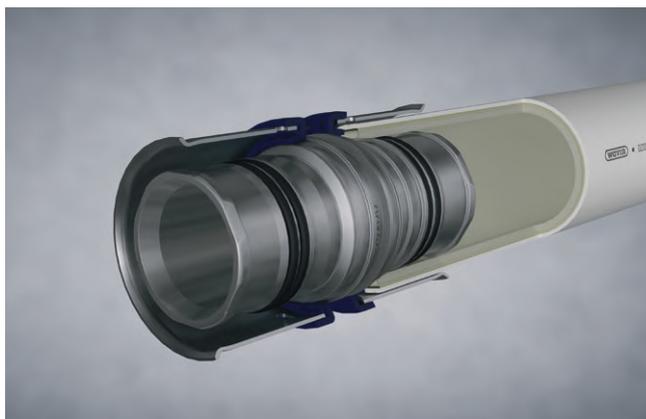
Geringe Einsteckkräfte durch das patentierte Sechskant-Querschnitt
